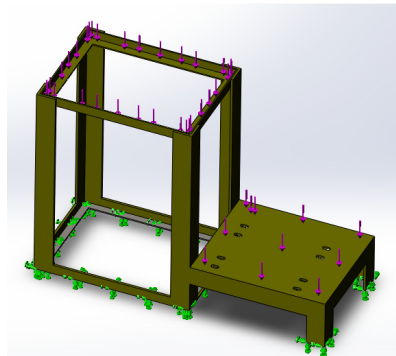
Colocación de restricción y de cargas en la estructura.
